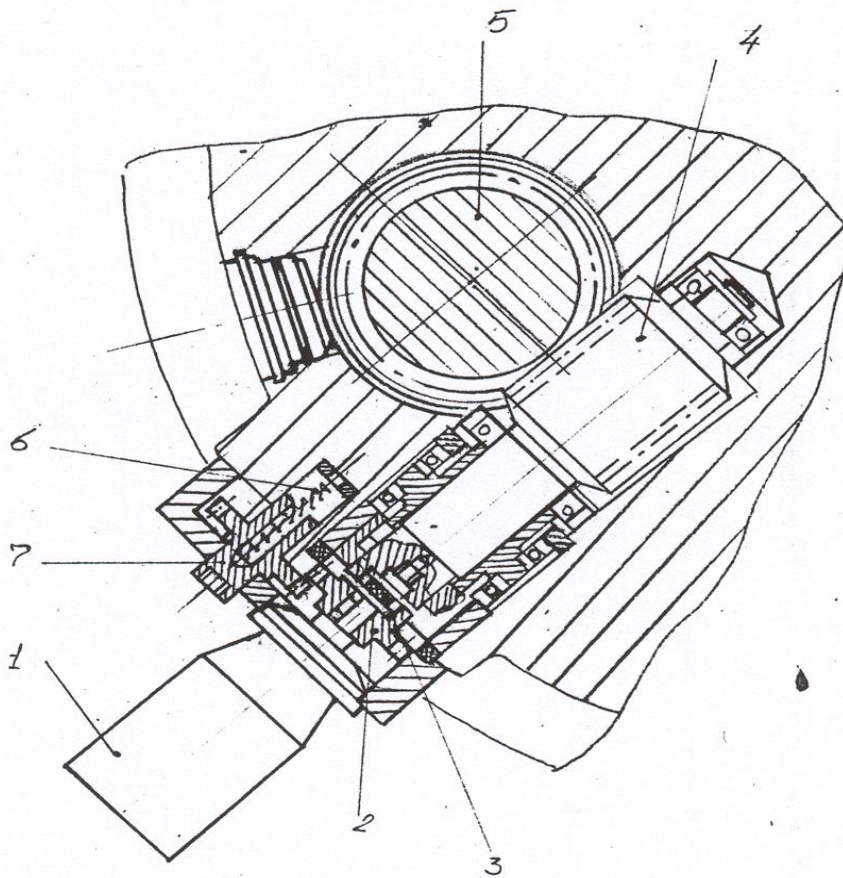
Привод делительно – поворотного стола с гидродвигателем: 1 – гидромотор, 2 – шестерня, 3 – разгонная муфта, 4 – червяк, 5 – колесо, 6 – пружина, 7 – шестерня – для ручного поворота
